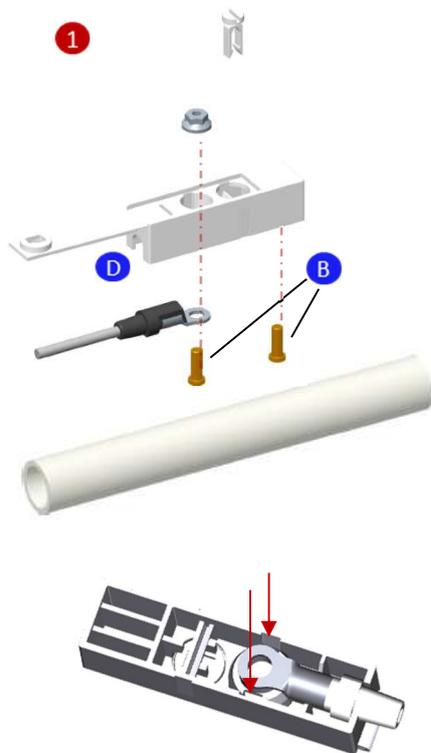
Führungshilfe für Befestigung des Fernfühlergehäuses mittels Kabelbinder
